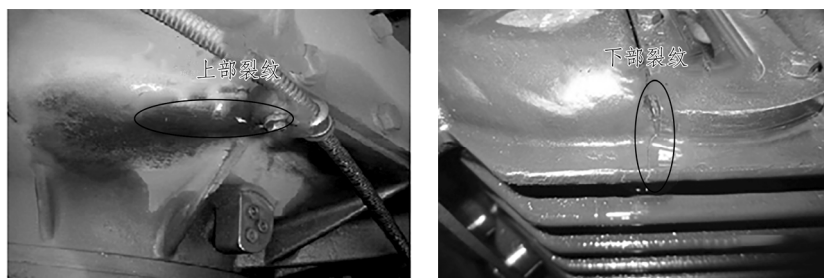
高速动车某齿轮箱箱体裂纹位置
